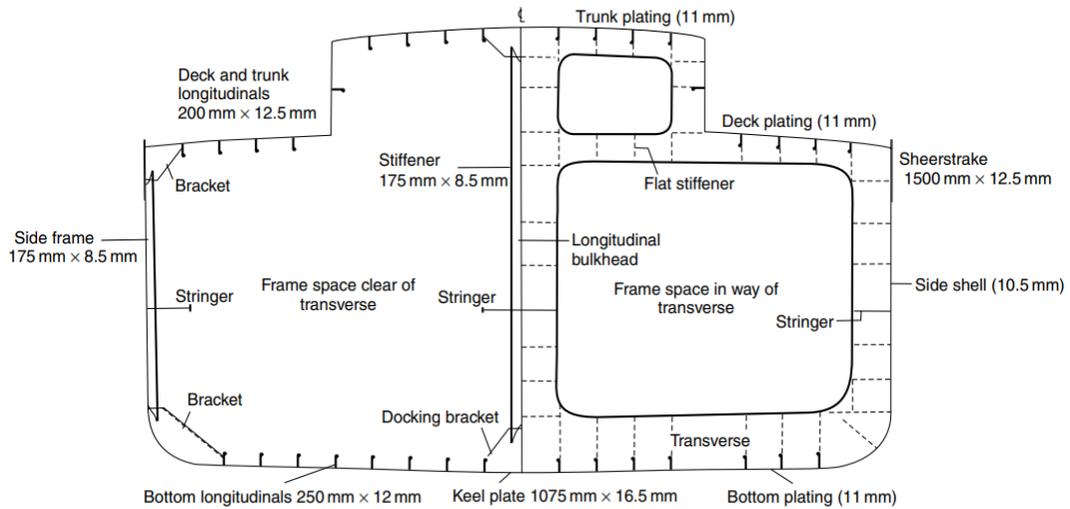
5 Konstruksi geladak (*Deck construction*)
